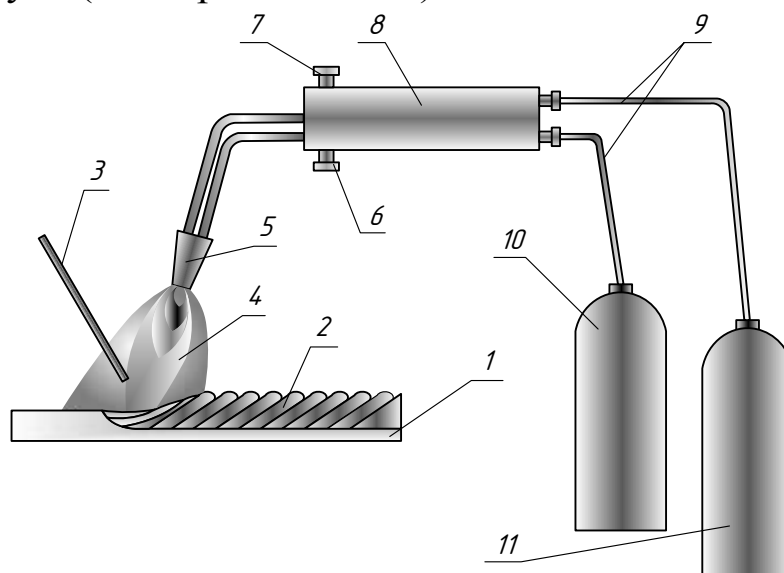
Схема газовой сварки и наплавки:
